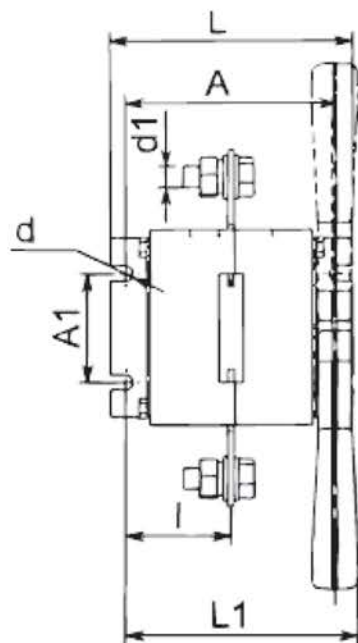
Выключатель-разъединитель однополюсный на два направления с боковой рукояткой.
